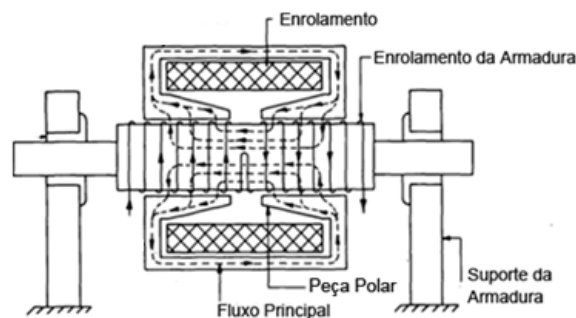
Fluxos principal do motor linear de corrente contínua. Adaptado de [18].
